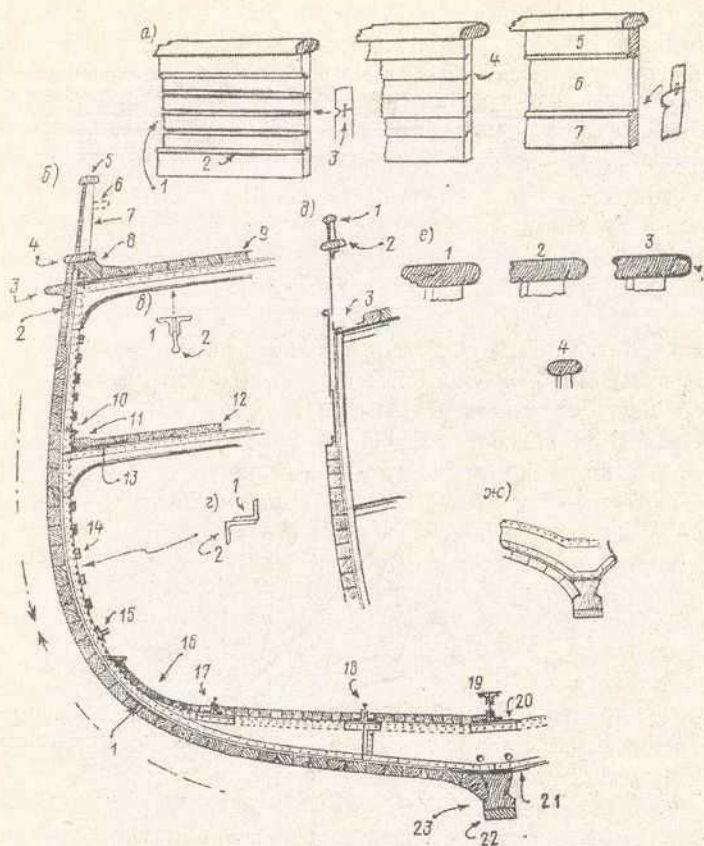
Конструкция корпуса клипера композитной постройки: а - разновидность деревянных фальшбортов; 1-соединение на вкладном шпунте; 2, 5, 7 - буртики; 3 - вкладной медный шпунт; 4 - наборная зашивка вгладь; 6 - декоративная филленка; б - шпангоут: 1 - железный, скуловой пояс; 2 - железный ширстрек; 3 - руслени; 4 - планширь толщиной 10,1 см; 5 - тиковый планширь; 6 - кафель- планка; 7 - деревянный фальшборт; 8 - тиковый ватервейс; 9 - тиковый или сосновый палубный настил толщиной 9,4-10 см; 10 - деревянная зашивка, закрывающая пространство между шпангоутами; 11 - ватервейс; 12 - сосновый палубный настил; 13 - палубный стрингер; 14 - бортовой рыбинс; 15 - бортовой кильсон; 16 - внутренняя сосновая обшивка; 17 - скуловой кильсон; 18 - боковой кильсон с интеркостельным листом между флорами; 19 - вертикальный кильсон; 20 - горизонтальный лист кильсона; 21 - горизонтальный лист киля;
